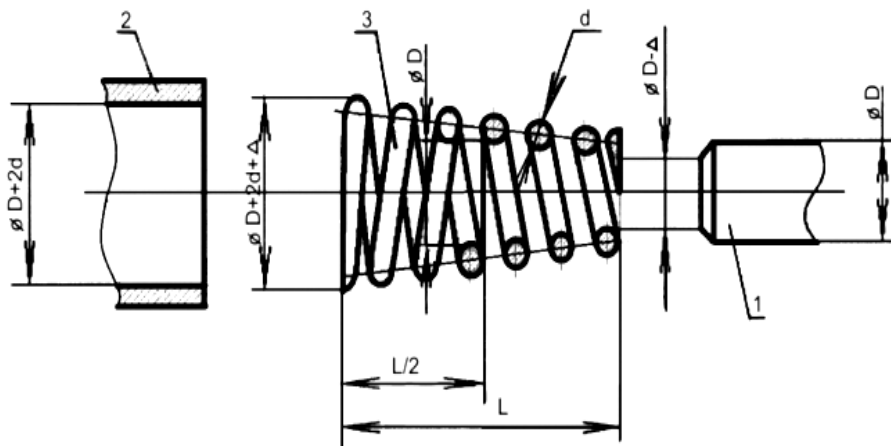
Конічний підшипник ковзання для зворотно-обертального руху
